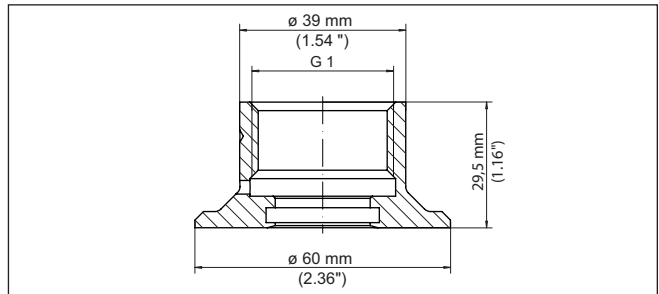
Dimensiones racor para soldar G1 (DIN 3852-A, ISO 228-1) con agujero de fuga
